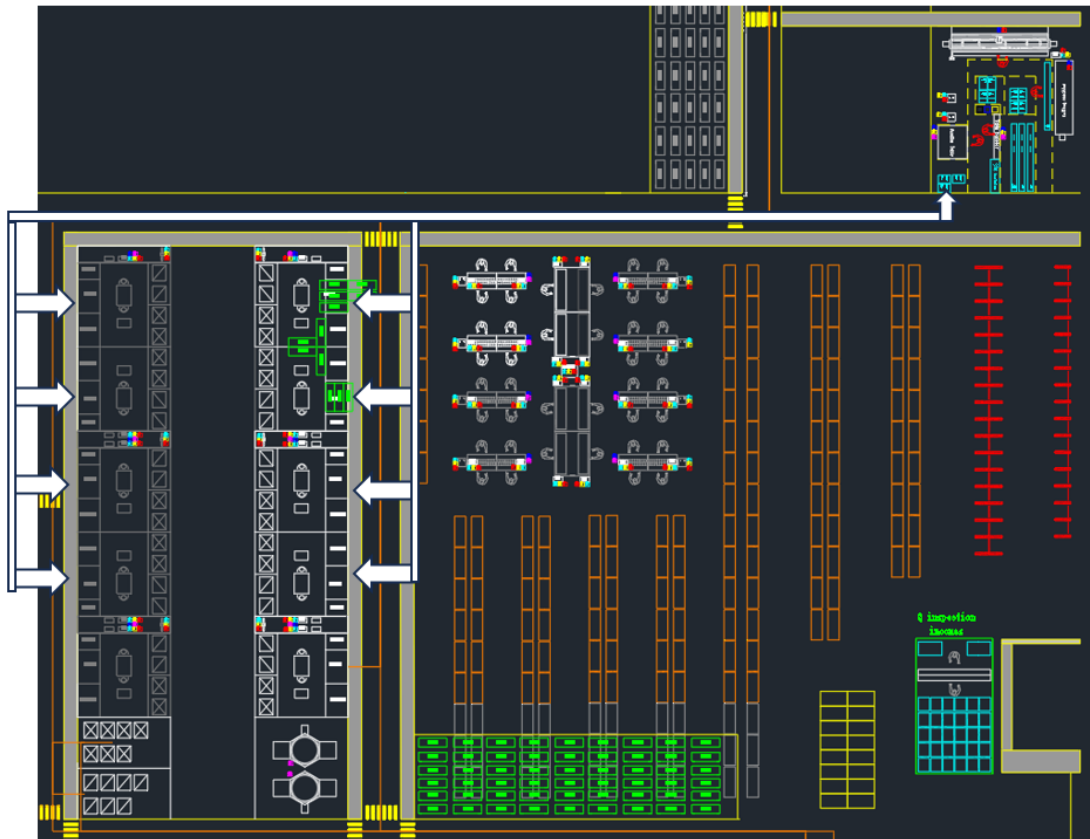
Movimentação entre os setores de Corte e Maquinagem de Perfis e Montagem de Cabines.
